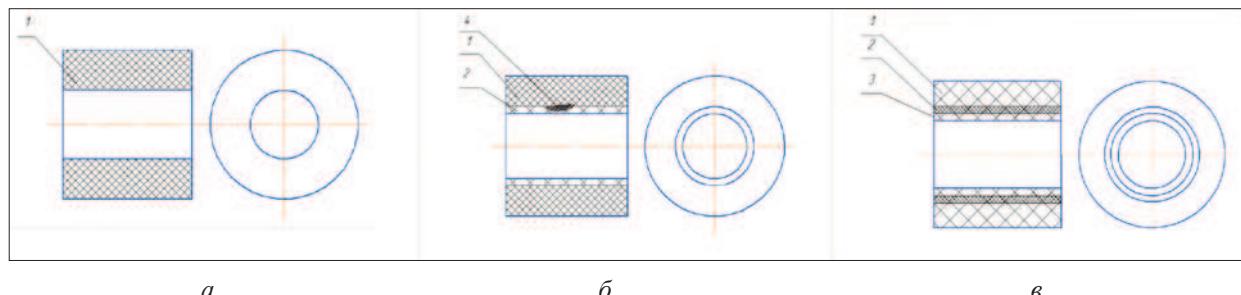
Схема конструкции стенки трубы системы вентиляции из ПКМ:
